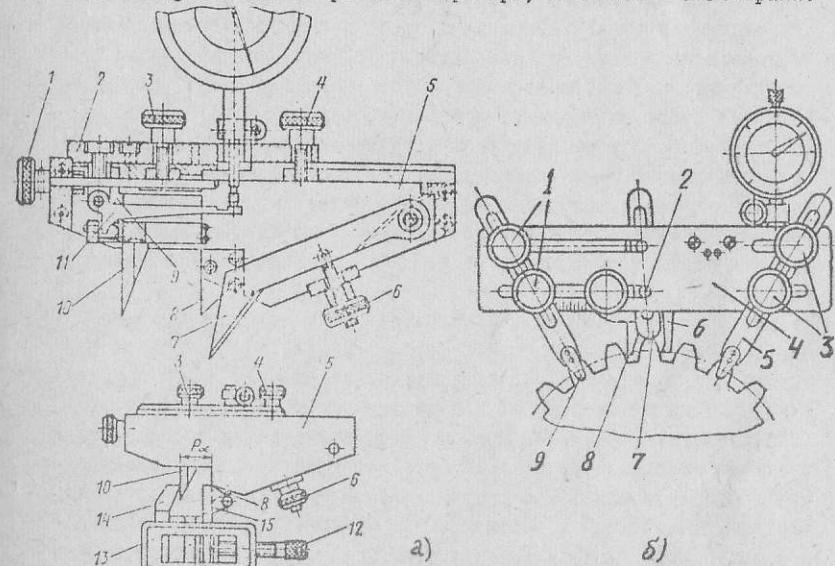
Схема шагомеров: а - для измерения шага зацепления; б - для измерения окружного шага.
